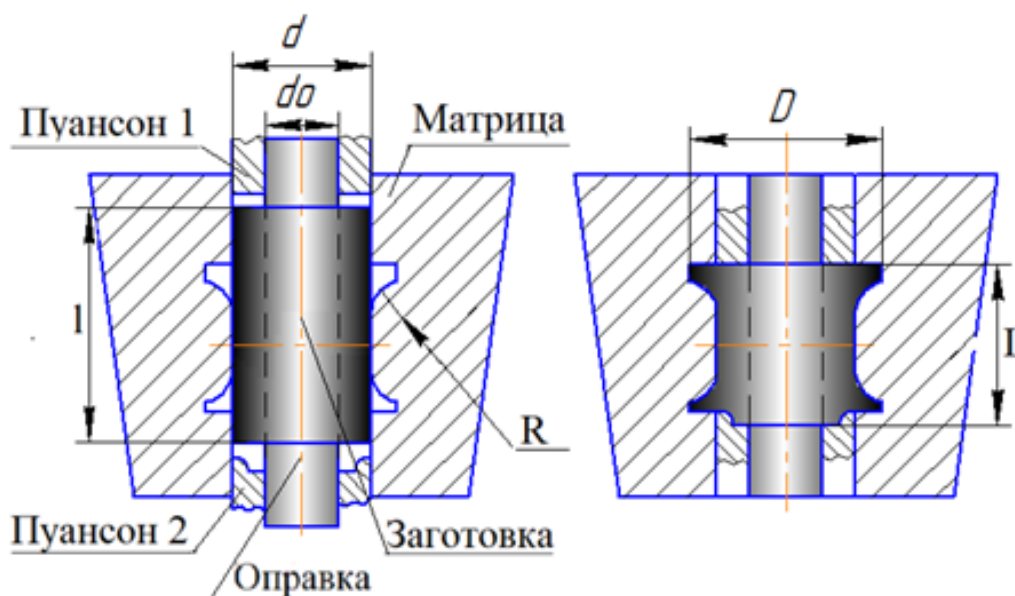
Схема штамповки деталей катушечной формы на оправке.
